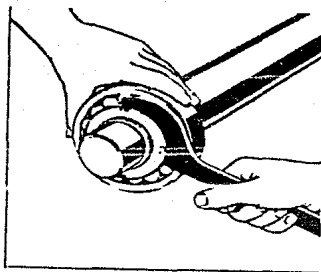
MONTAJE DEL RODAMIENTO SOBRE EL MANGUITO
